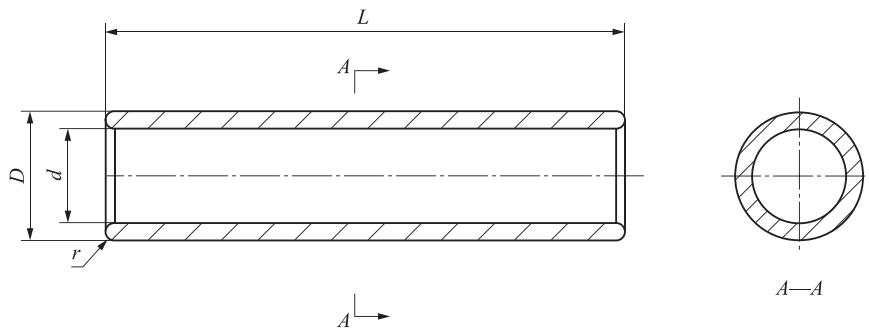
铜或铝连接管 (GT 型或 GL 型) 形状
